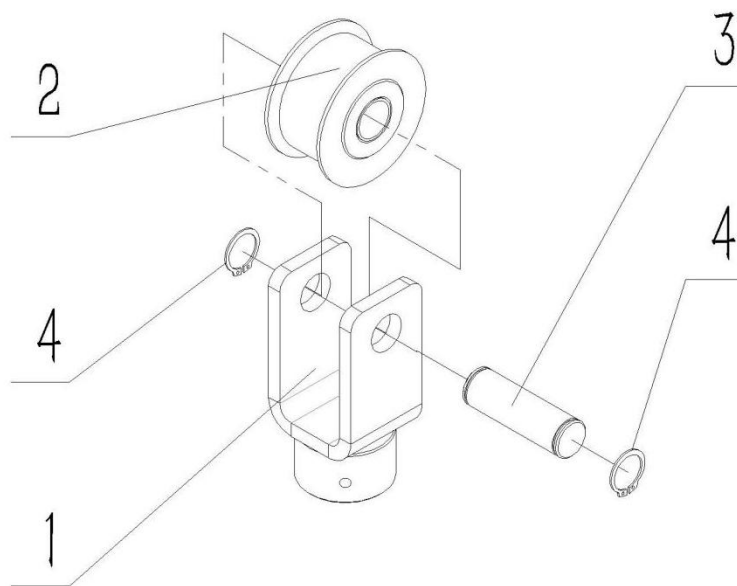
Explosionszeichnung des Kettenradrahmens des Hebebocks
